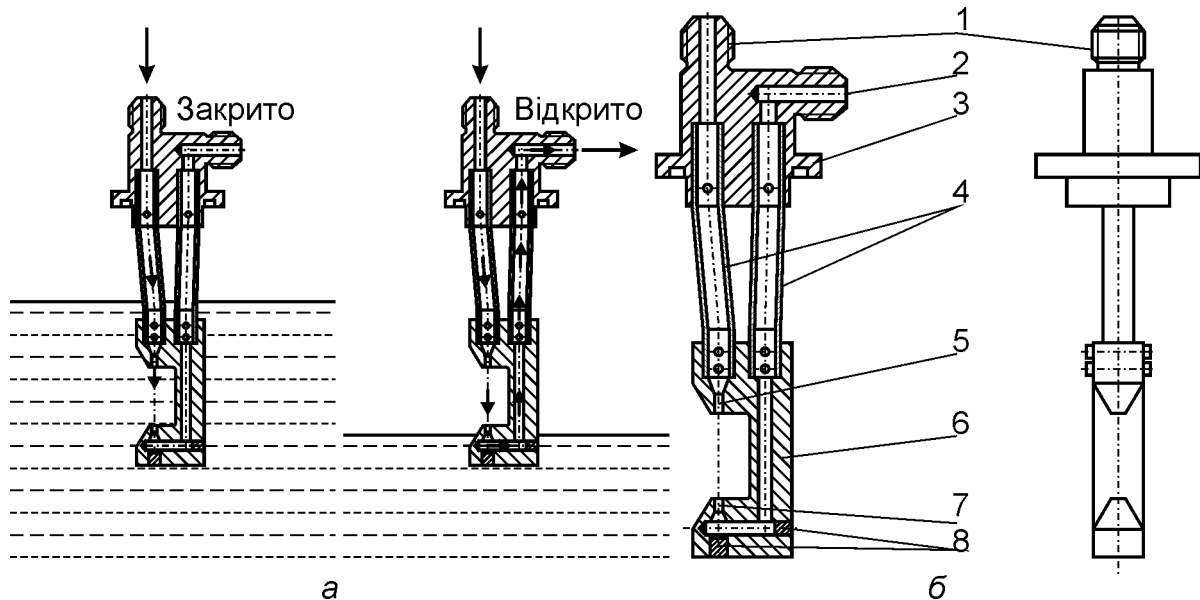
Струминний датчик рівня (МиГ-29): а — схема роботи; б — конструкція; 1 — штуцер підведення КП; 2 — штуцер відведення КП; 3 — корпус; 4 — трубки; 5 — сопло; 6 — скоба; 7 — приймач; 8 — заглушки
